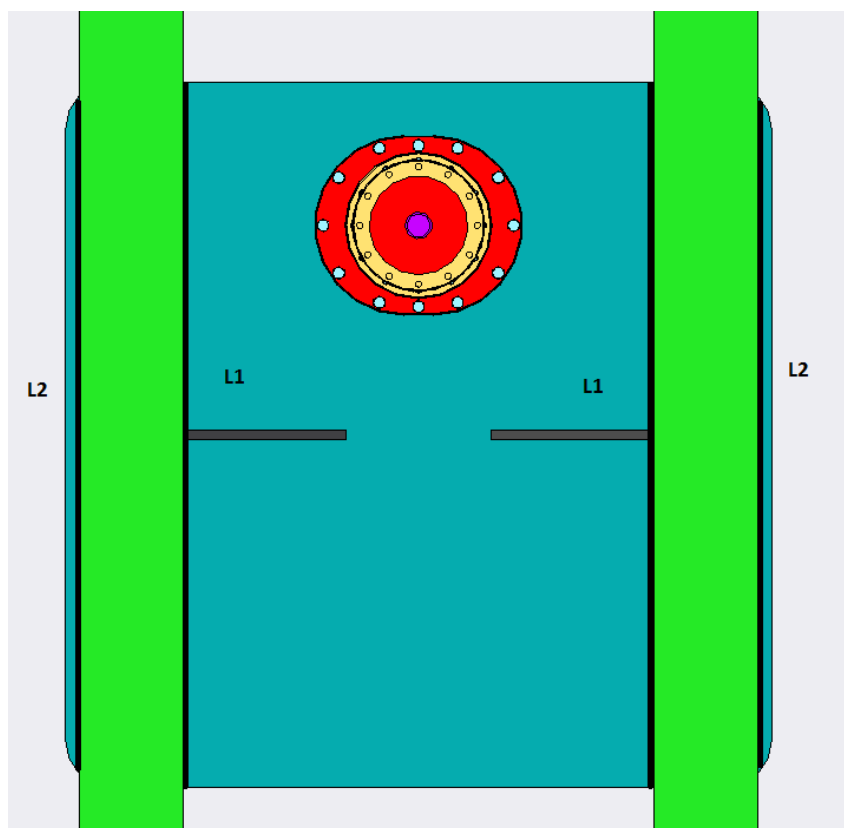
Cordones de soldadura unión pluma-placa superior (redimensionamiento).
